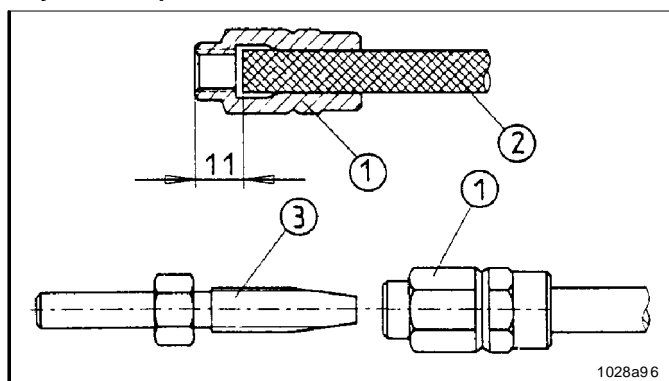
Prémontage de la douille filetée et de l'embout sur le tuyau haute pression
